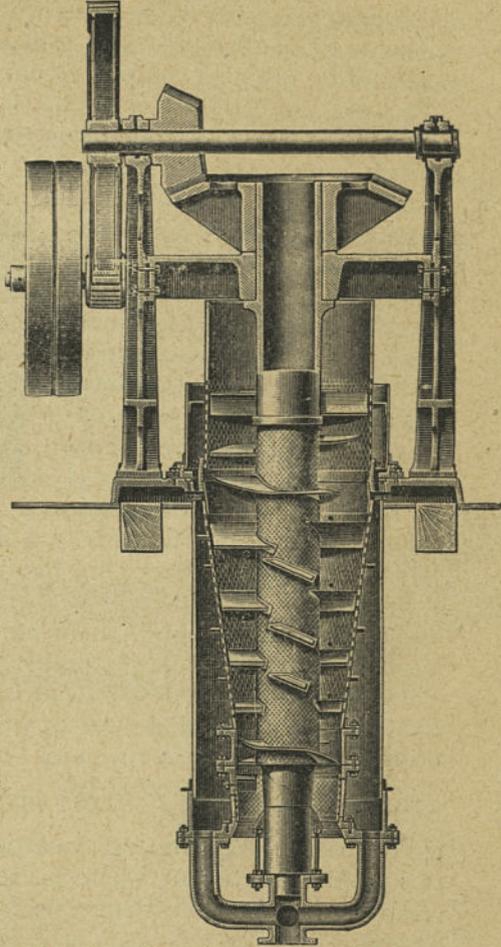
Presse Bergreen (Construction Sangerhausen).
